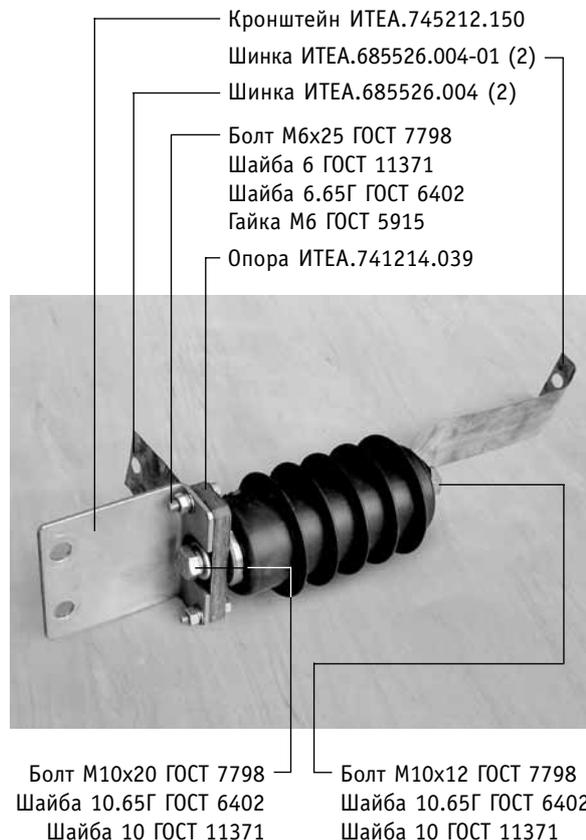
Установка ОПН в сборе с элементами крепления на ошиновку ВВ/TEL 10-20/1000
